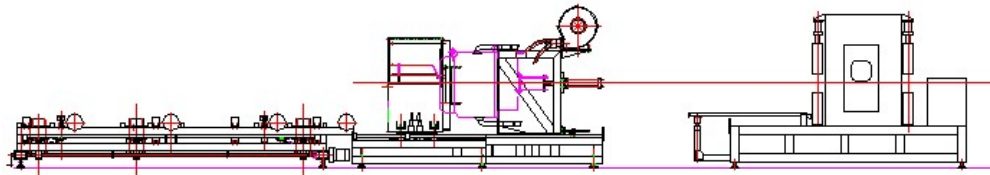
Sierra y máquina de acampanado para tubo de PVC.
